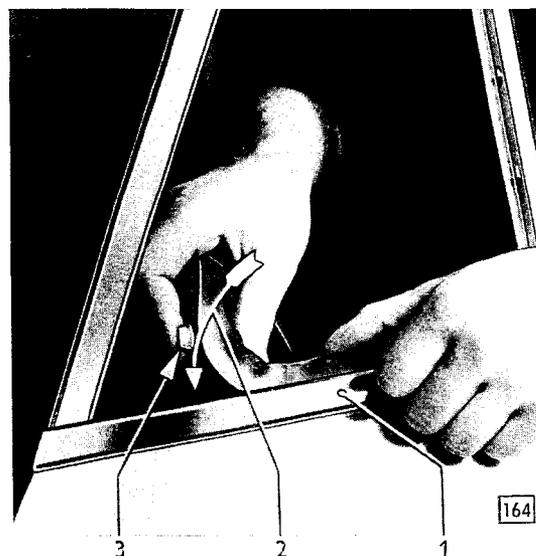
Vordere Dichtung mit geschlossenem Profil unter hintere Dichtung einführen
